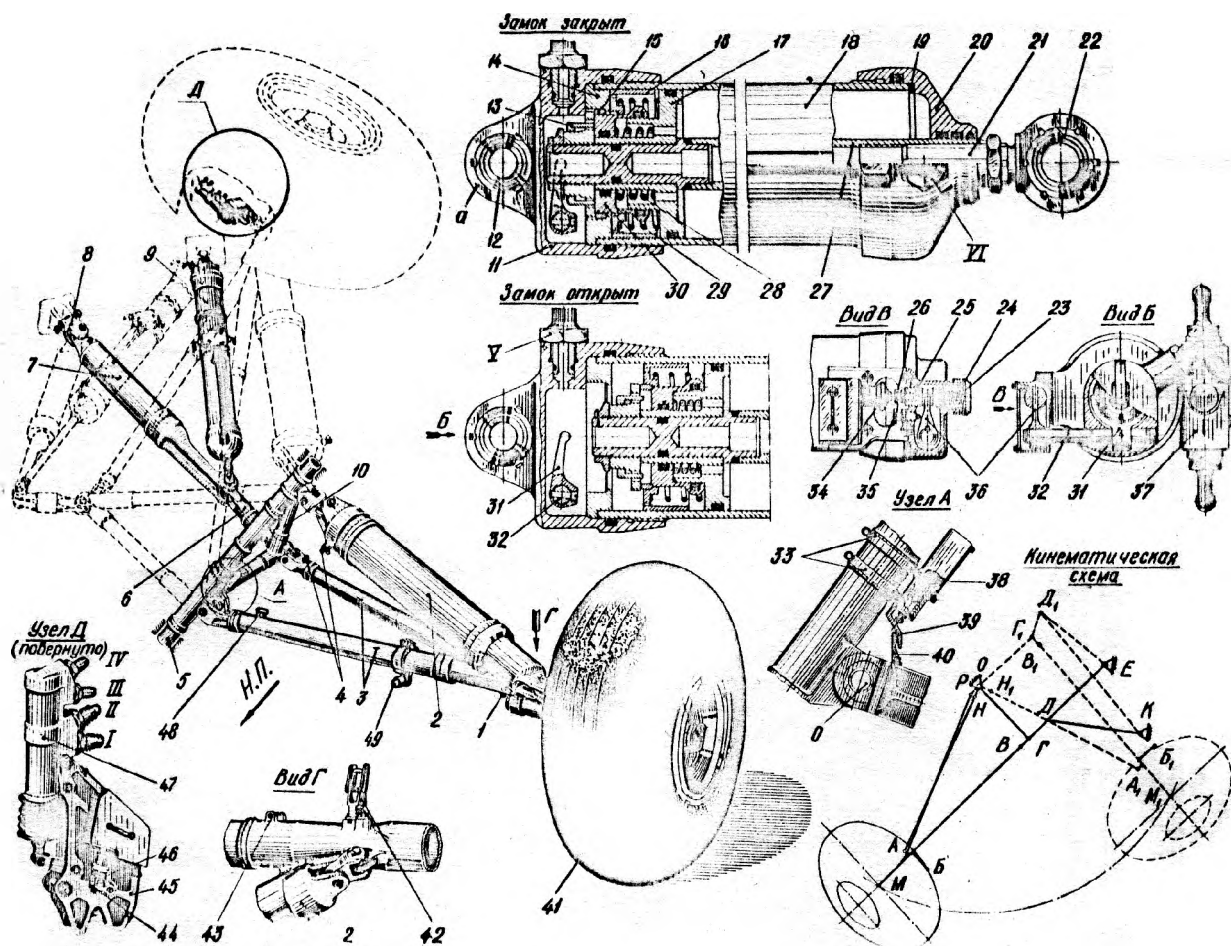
Главная стойка шасси с механизмом уборки и выпуска вертолета Ми-24А [13]:
